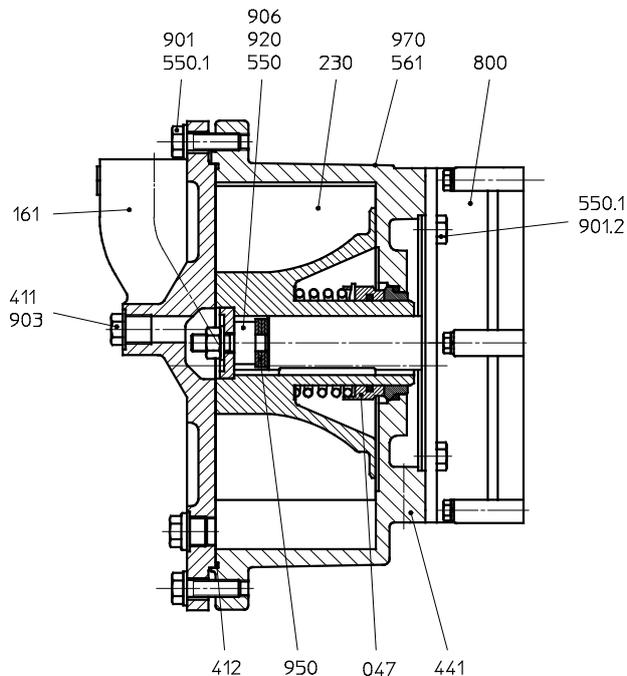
Schnittzeichnung VG-255 – Gewindeausführung
